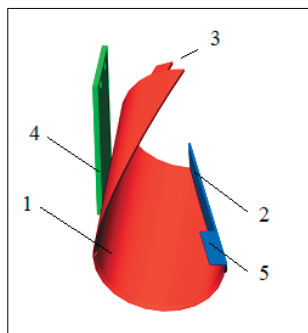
Схема рабочего органа для прецизионной обработки почвы: 1 – усеченный цилиндрический отвал; 2 – направляющая доска; 3 – сталкиватель; 4 – стойка; 5 – крыло
